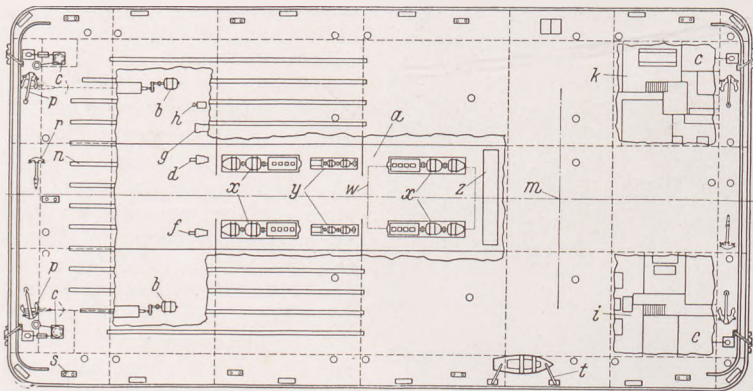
Ponton des 250 t-Schwimmkrans Brest. Grundriß.
